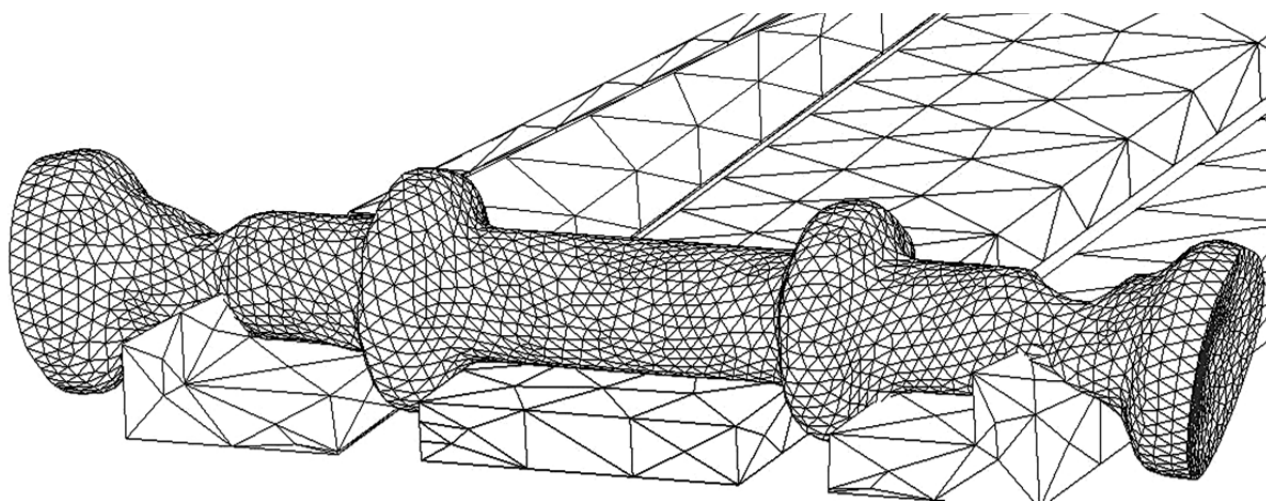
Конечно-элементная модель заготовки (конечная форма)
